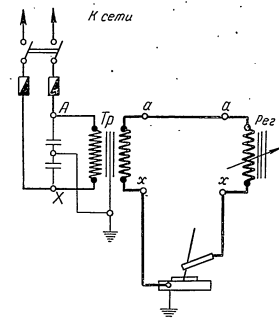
Схема соединения обмоток трансформатора типа СТЭ-24-У и регулятора
